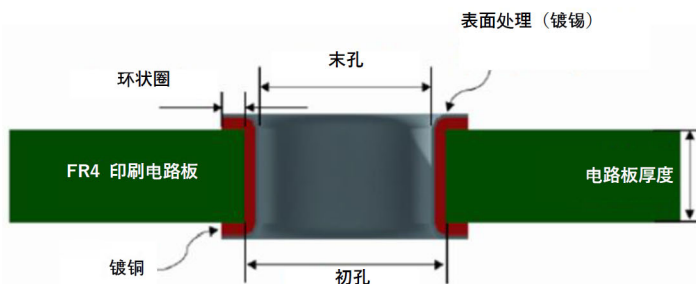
PCB 压合式孔的定义和每个压合式孔周围的组件禁入区
